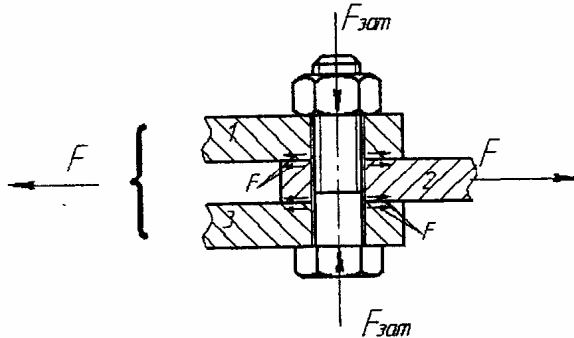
Схема для расчета болтового соединения, нагруженного сдвигающей поперечной силой
